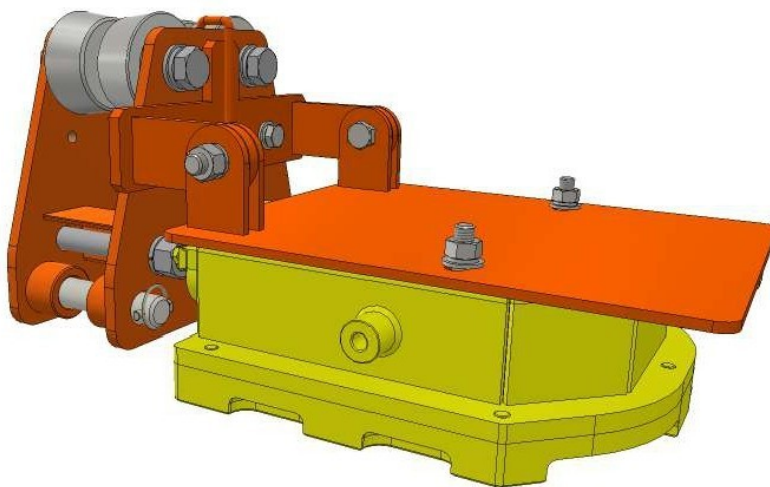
а. Держатель для светильника, установленный на тележке типа 1-606 или 1-605.
